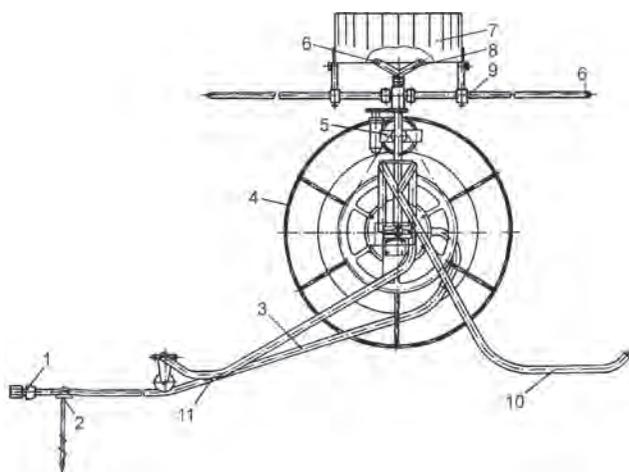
Схема общего вида шлангового дождевателя ДШ-1: 1 – узел подсоединения; 2 – якорь; 3 – водопроводящий шланг; 4 – катушка; 5 – редуктор; 6 – сопла с рассекателями; 7 – корона; 8 – дождевальная аппаратура; 9 – сегнерово колесо; 10 – лыжи; 11 – опора с направляющим роликом
